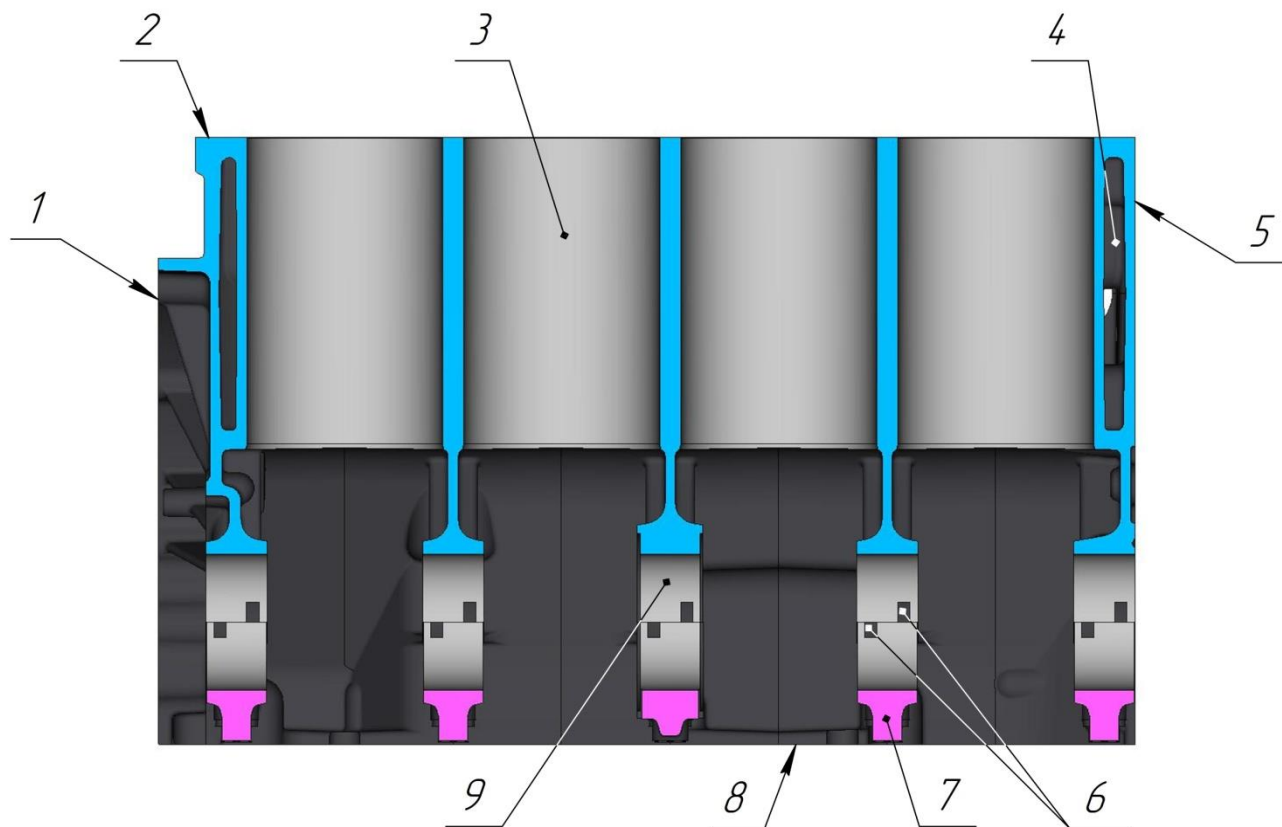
Блок цилиндров. Продольный разрез по оси цилиндров:
